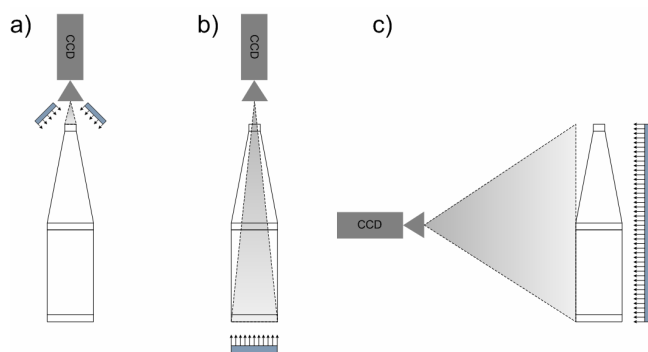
Prostorové uspořádání inspekčního systému
